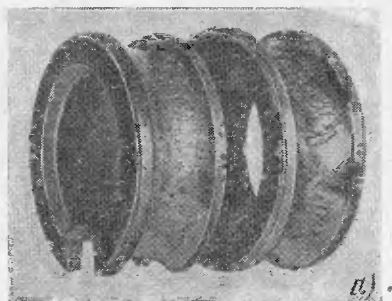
Усталостное выкрашивание металла на рабочих поверхностях подшипников.
